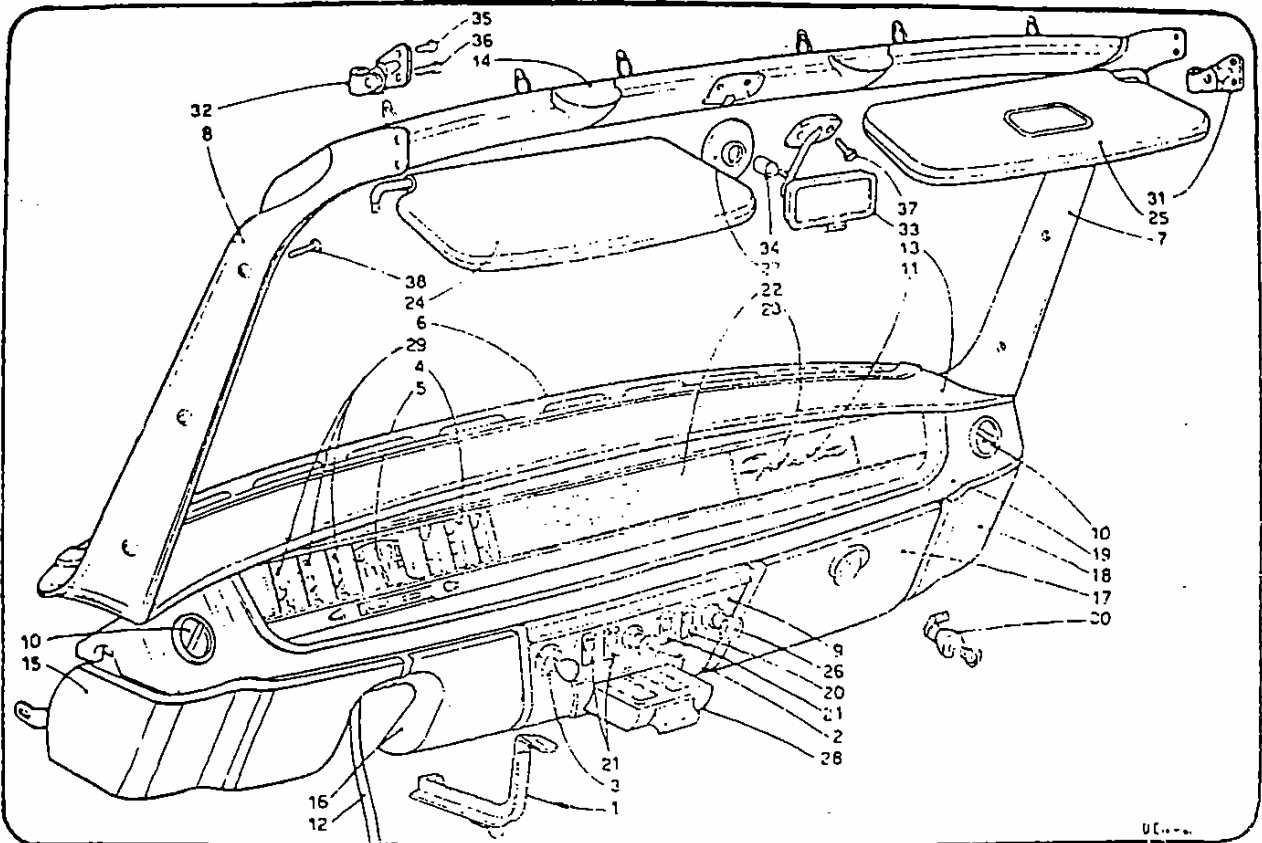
/11 - Equipement planche de bord - Rembourrages (du Catalogue Pièces Détachées).
